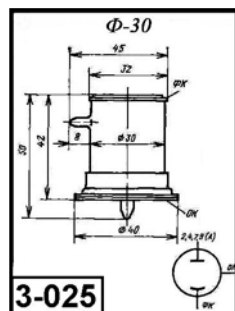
Внешний вид и габаритные размеры фотоэлементов серии Ф-XX
